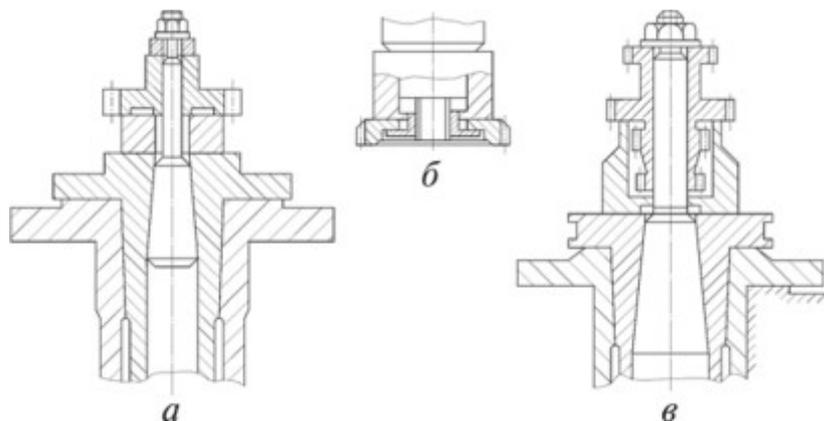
Схемы установки зубчатых колес при зубодолблении: а, б — одновенцового; в — многовенцового
